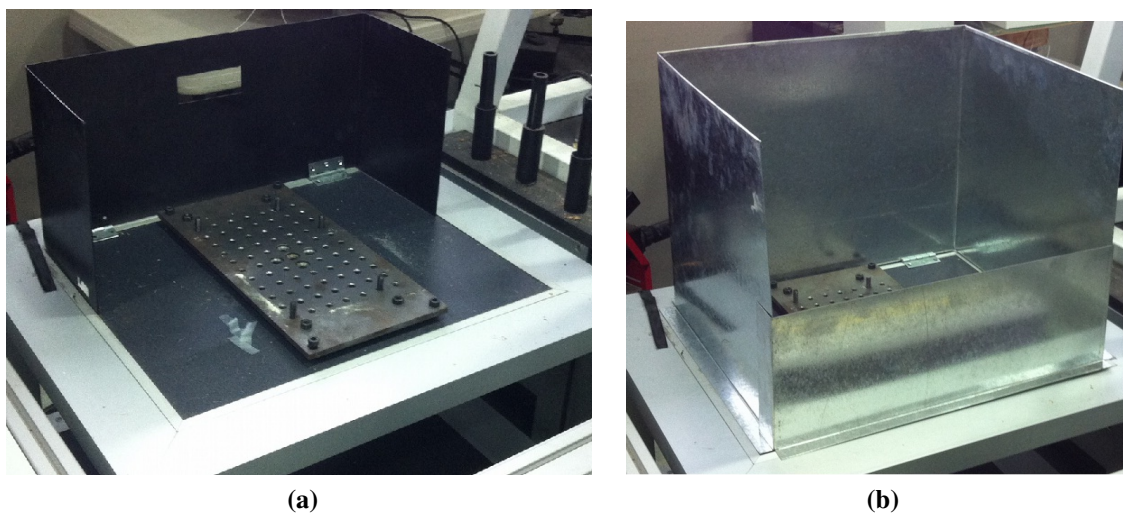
Protección para la cámara de soldadura. a) Sistema inicial. b) Sistema de protección mejorado.
